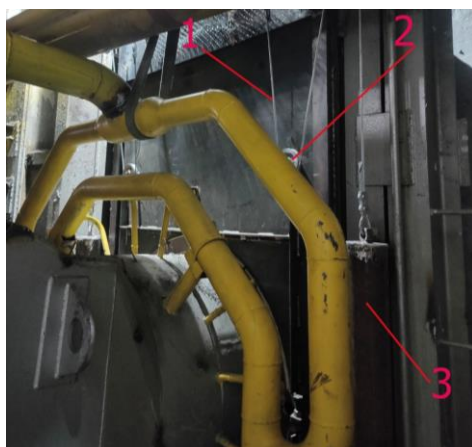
Система противовеса щита (1 – трос; 2 – шкиф; 3 – один из двух грузов)
